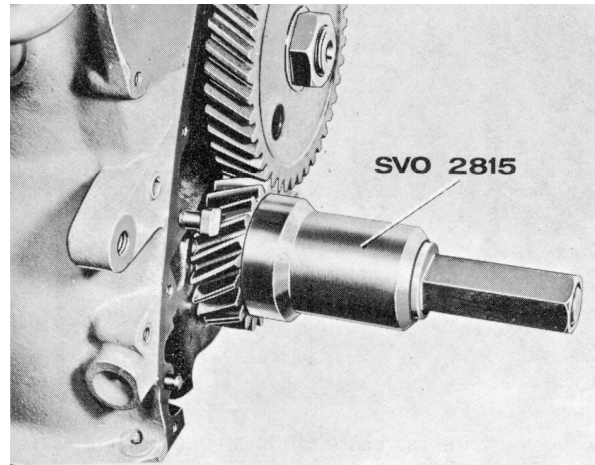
Montering av vevaxeldrev (6-cyl. motor)
